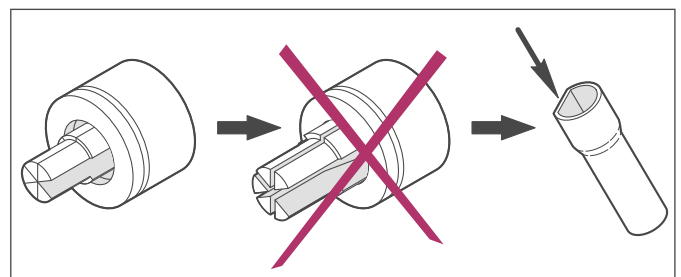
Endommagement du tube par une tête d'expansion défectueuse
